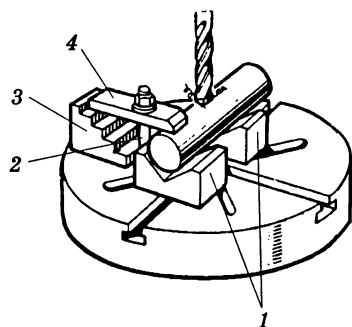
Установка и закрепление валика с помощью ступенчатой опоры:
